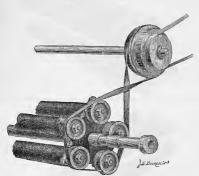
Disposition d'une extrémité du tambour laineur de la machine Grosselin.
